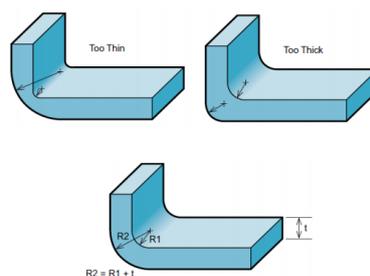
Radio recomendado para el diseño de piezas de inyección. (Fuente: <https://icomold.com/design-guidelines/>)
